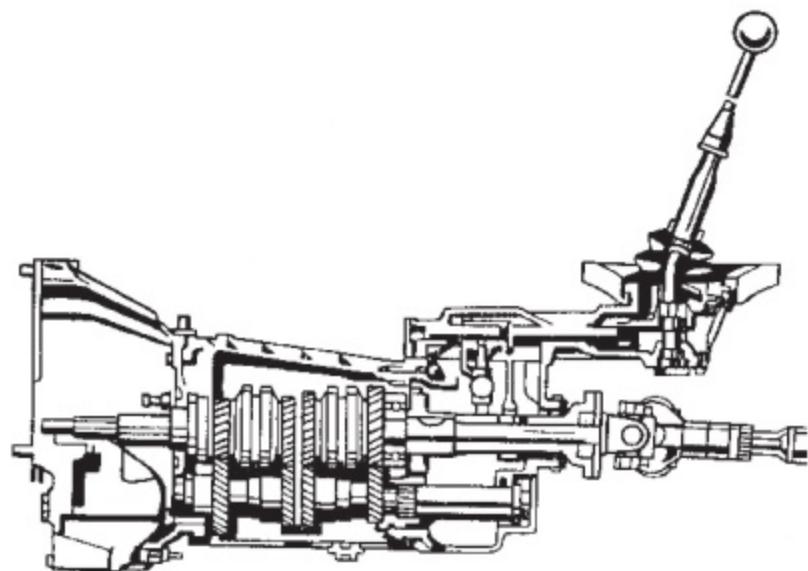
Коробка передач с механизмом управления, имеющим промежуточный элемент — переключатель, расположенный в удлиненной верхней крышке коробки передач
